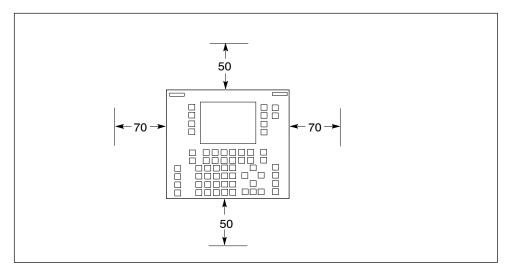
Abstandsmaße beim Einbau des C7-635 Key
